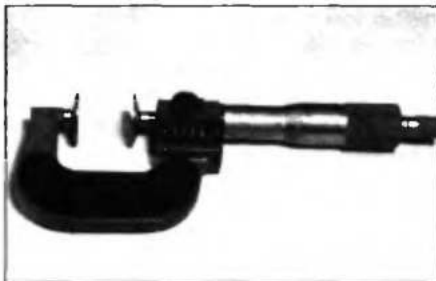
Специальный микрометр для измерения ширины перемычек между канавками поршня и другими элементами деталей
